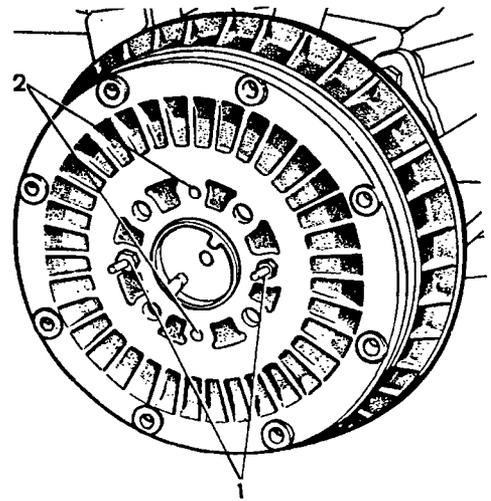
Тормозной барабан заднего тормоза: 1 - болты крепления барабана к полуоси; 2 - резьбовые отверстия для установки болтов 1 при снятии барабана
